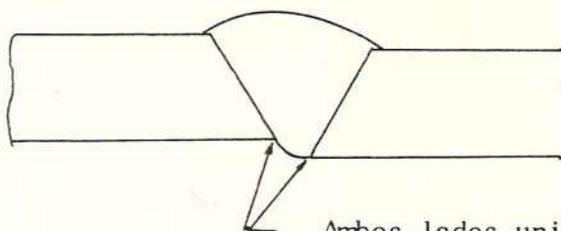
Penetración inadecuada en la raíz de la soldadura
